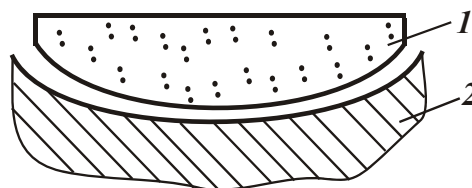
Шлифование вогнутых сферических поверхностей: 1 – шлифовальный круг; 2 – обрабатываемая деталь.
